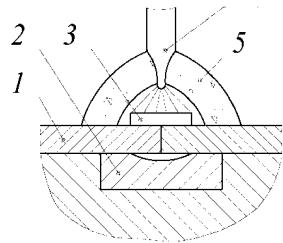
Схема механизированной сварки меди угольным электродом под флюсом
